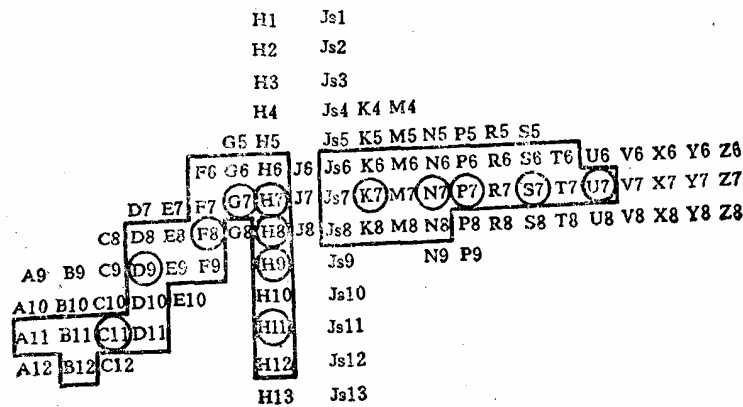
8 优先、常用和一般用途的孔公差带 (尺寸≤500mm)
